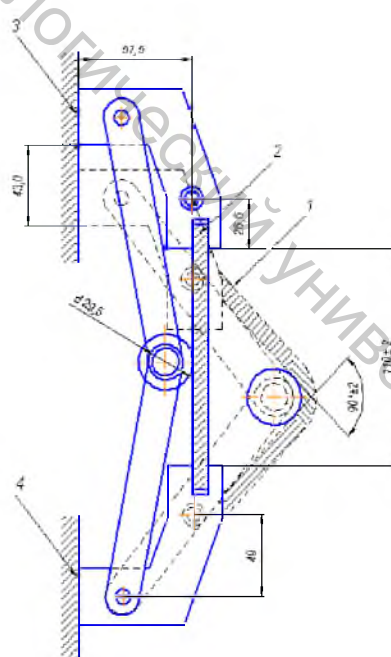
Принципиальная схема узла испытаний на установке УИМИ-1
